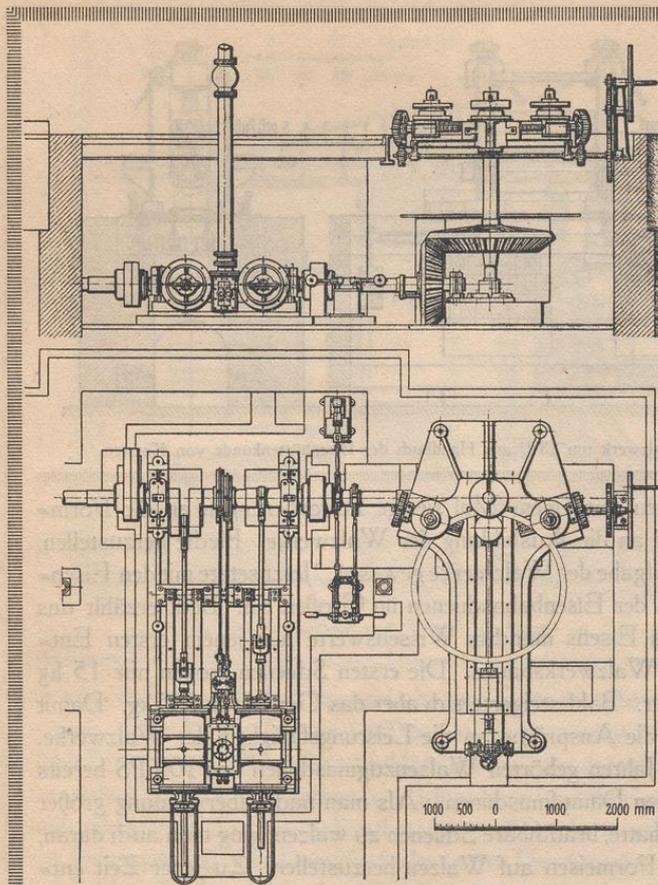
u. 24. Bandagenwalzwerk mit Zwillingmaschine
